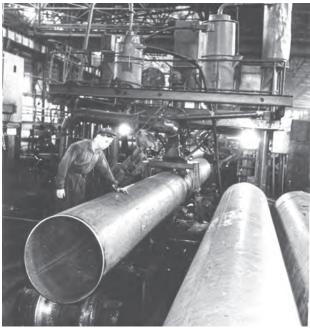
Цех автоматической сварки Харцызского трубного завода
